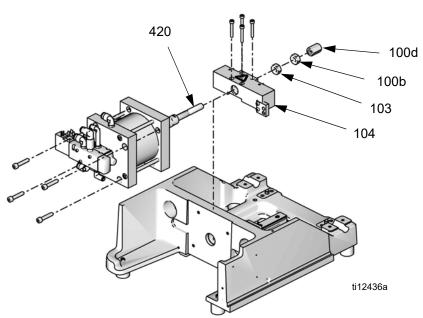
Installation de l'HydraCheck - Base à rapport fixe
